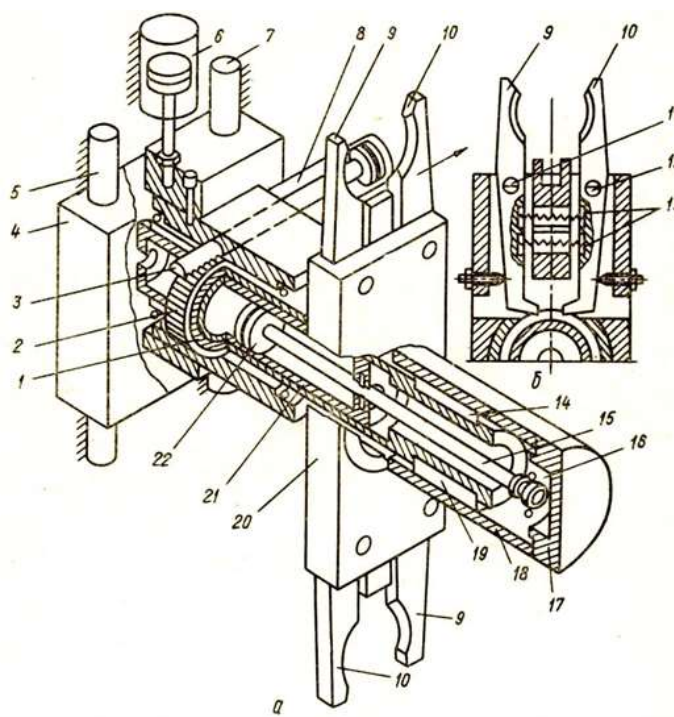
Схема автооператора для зміни інструмента на верстаті з ЧПК.
